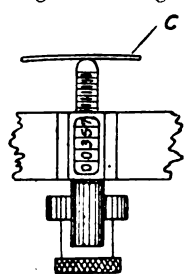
Mikrometerschraube mit Gangzähler. Oben die Blattfeder *c*.
